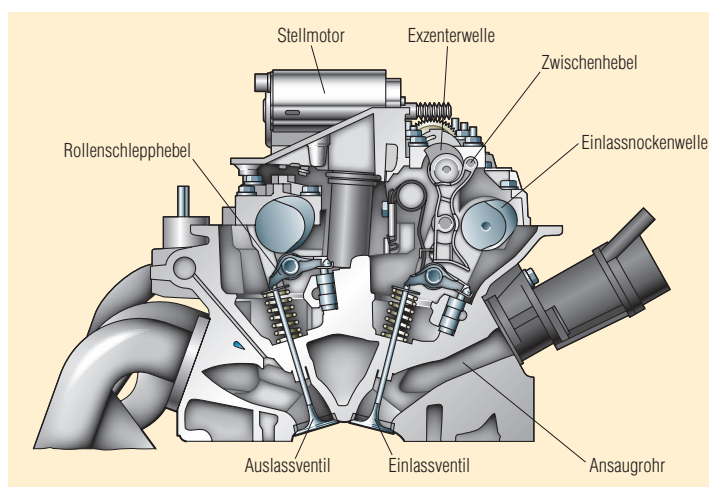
Schnitt Zylinderkopf mit Valvetronic.
